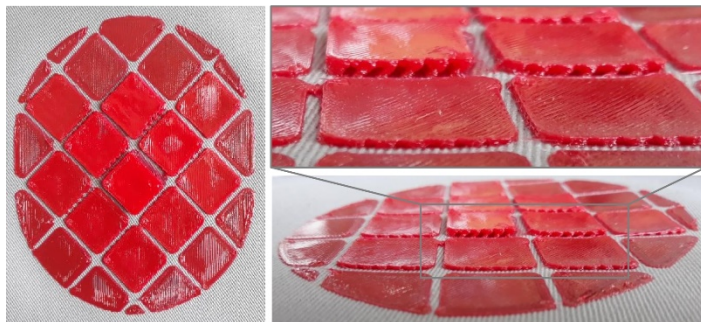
D-gedruckte Abriebschutzstruktur mit kompressiblen Dämpfungsstegen auf einem Baumwollgewebe
